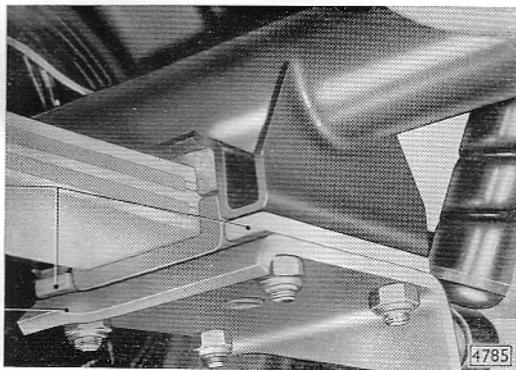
Befestigung Hinterachse an Hinterfeder
